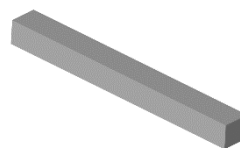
Quick wall wood - sloupek dělený rohový 180; 210 Dub
